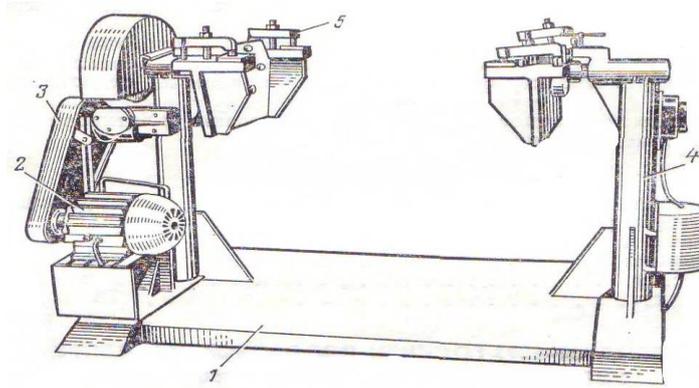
Стенд модели ОПР- 1881.05 для разборки и сборки коробок
